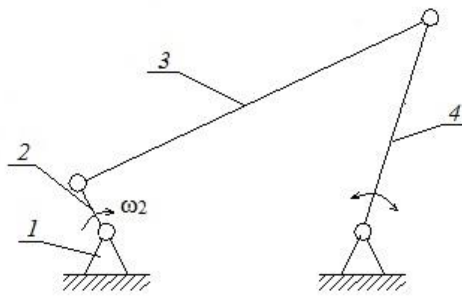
Кривошипно-балансирний механізм:
